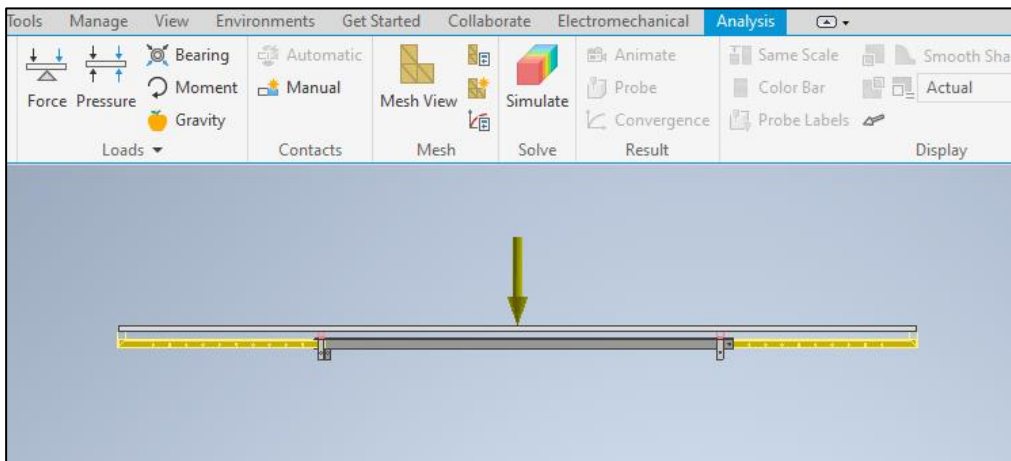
Vista inferior de la plancha apoyada en los 4 soportes
